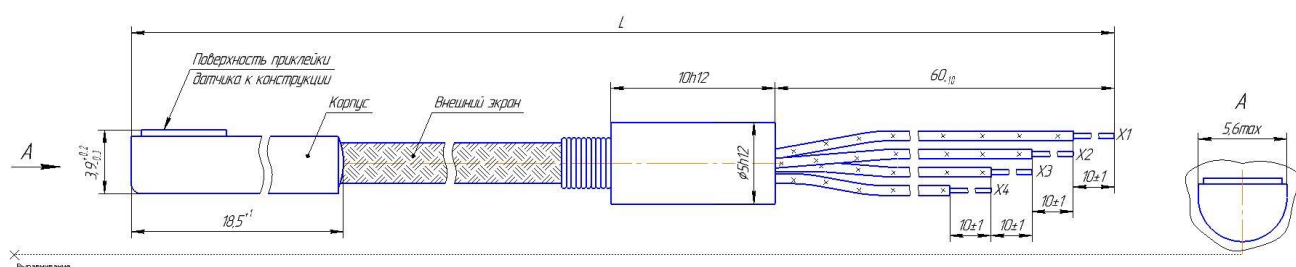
Габаритные и установочные размеры датчика исполнений ЦДТ 1-06 – ЦДТ 1-09
